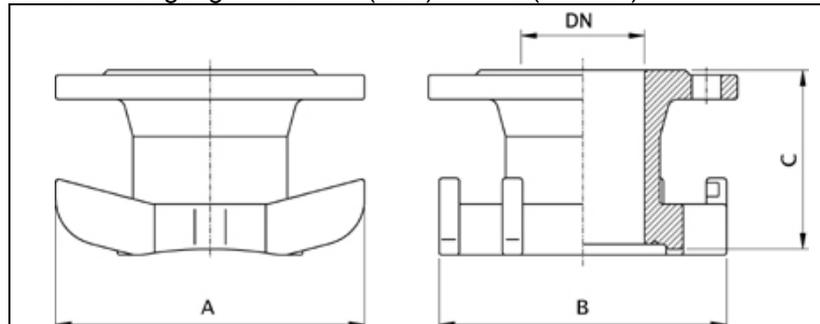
Doppelbügel-Anbohrschelle mit Flanschabgang DN80/PN4 (Gas) / PN16 (Wasser)
